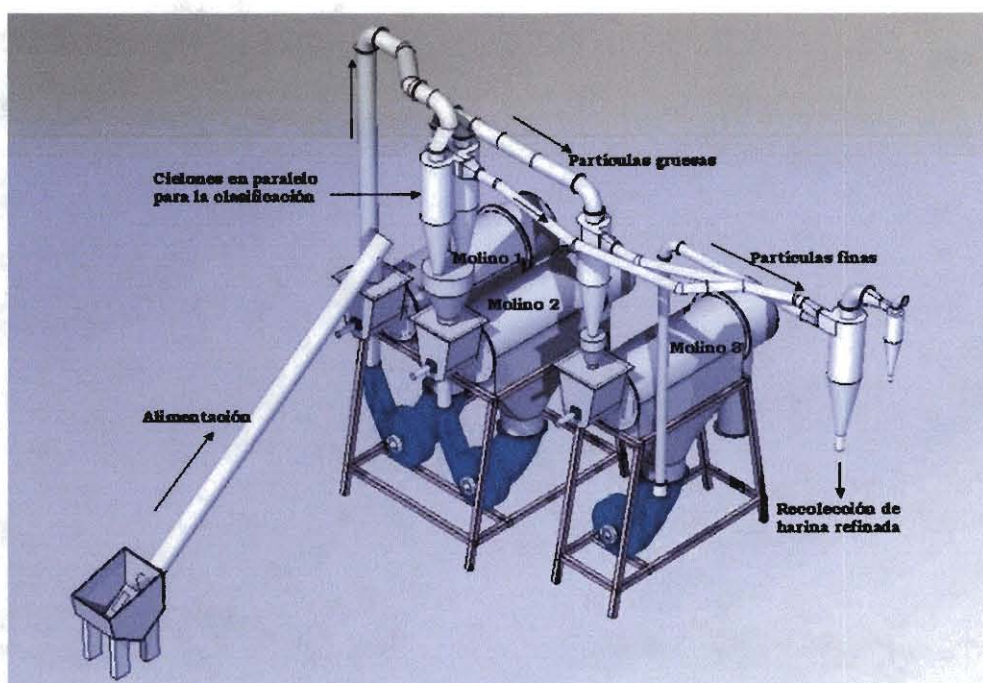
Esquema de diseño propuesto para la planta continua de refinación.
